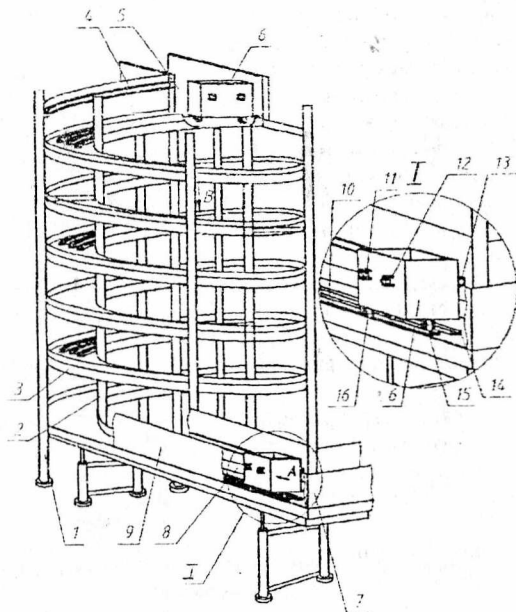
Загальний вигляд гвинтового роликового конвеєра контейнерного типу
